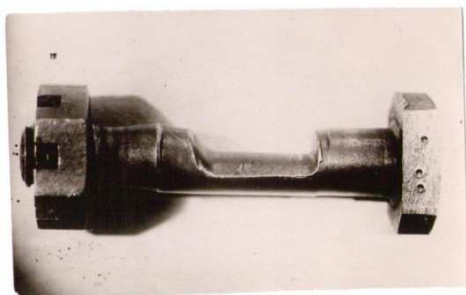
Интенсивно изношенный болт крепления щитка закрылок двигателя самолета за несколько часов полета
